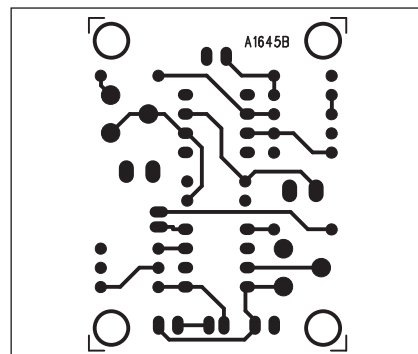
Obrazec desky spojů vysílače (strana BOTTOM)
